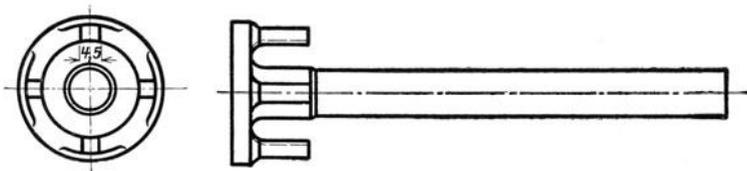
Kegel mit ausgefrästen Führungsrippen.
